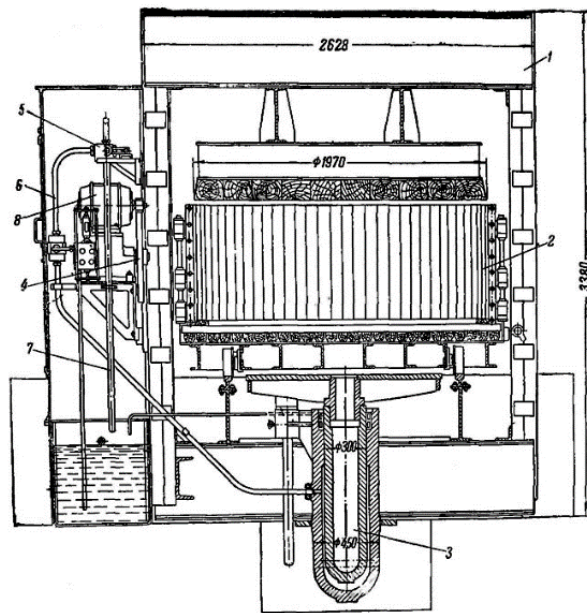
Розріз гідравлічного преса з нижнім тиском: 1 – станина; 2 – дренажний кошик; 3 – гідравлічний циліндр із пресувальною плитою; 4 – гідравлічний насос; 5 – блок керування пресом; 6 – трубопровід блока керування пресом; 7 – зливна труба; 8 – електродвигун.
